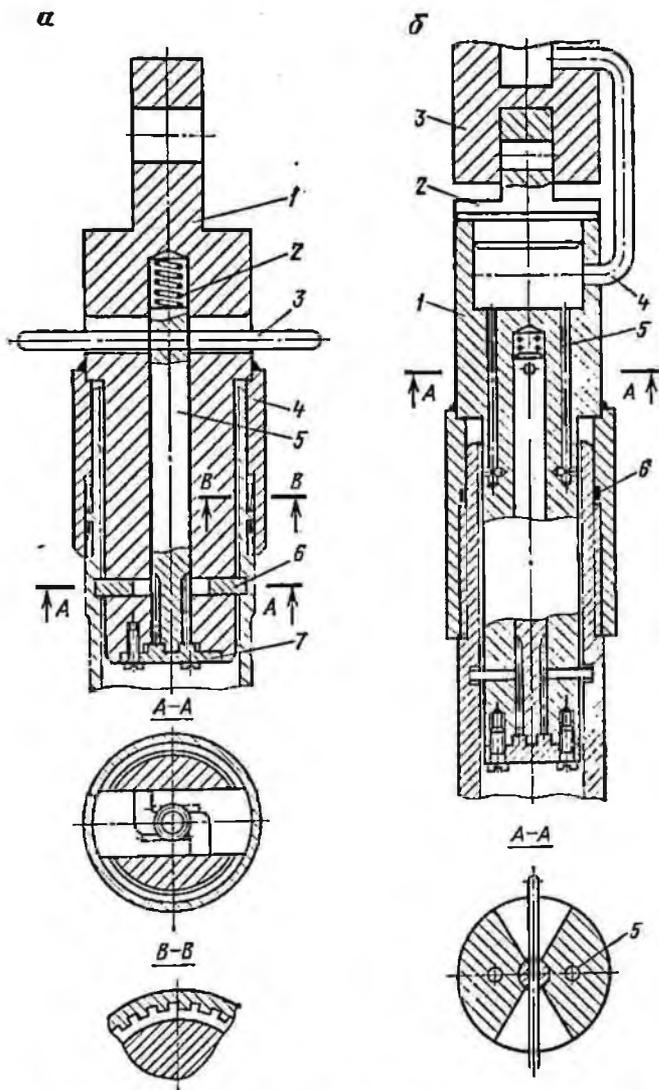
Элеватор для соединения полых шнеков с вращателем:
